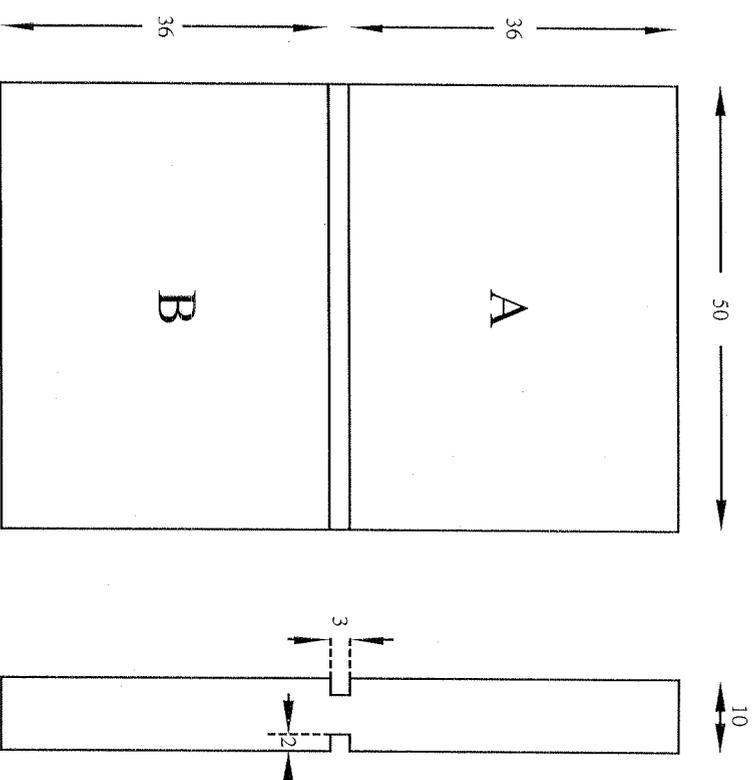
COMPROBADOR DE LÍQUIDOS PENETRANTES
